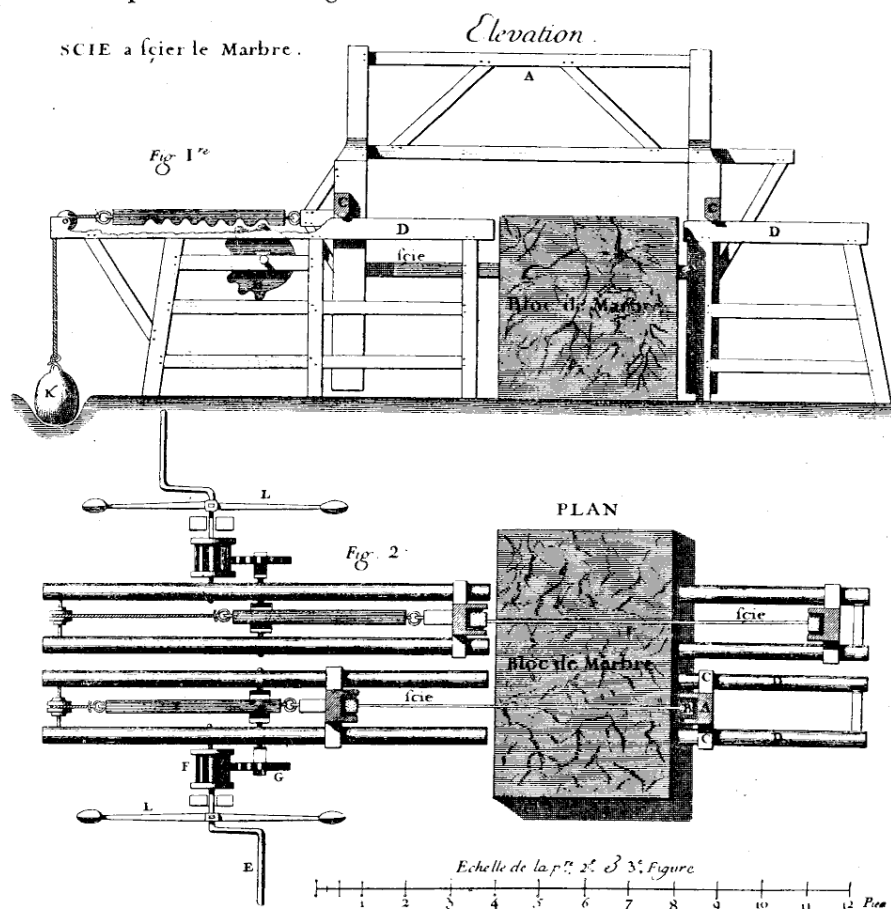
Machine à scier le marbre au XVIII^e siècle (BÉLIDOR).
